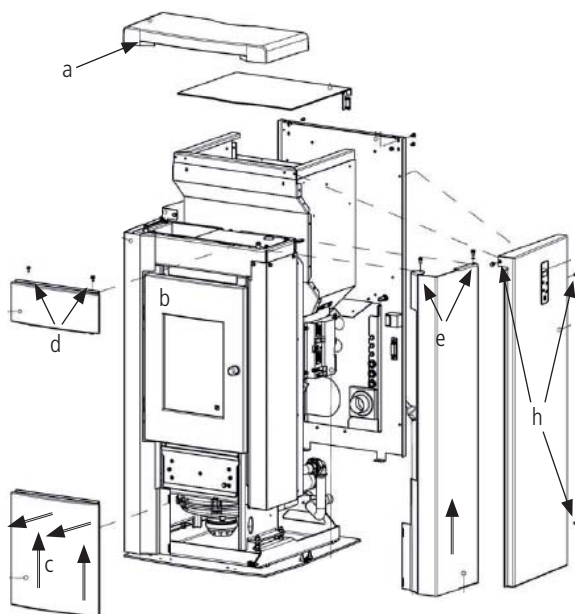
Explosionszeichnung UMBRA, Demontage der Verkleidung
